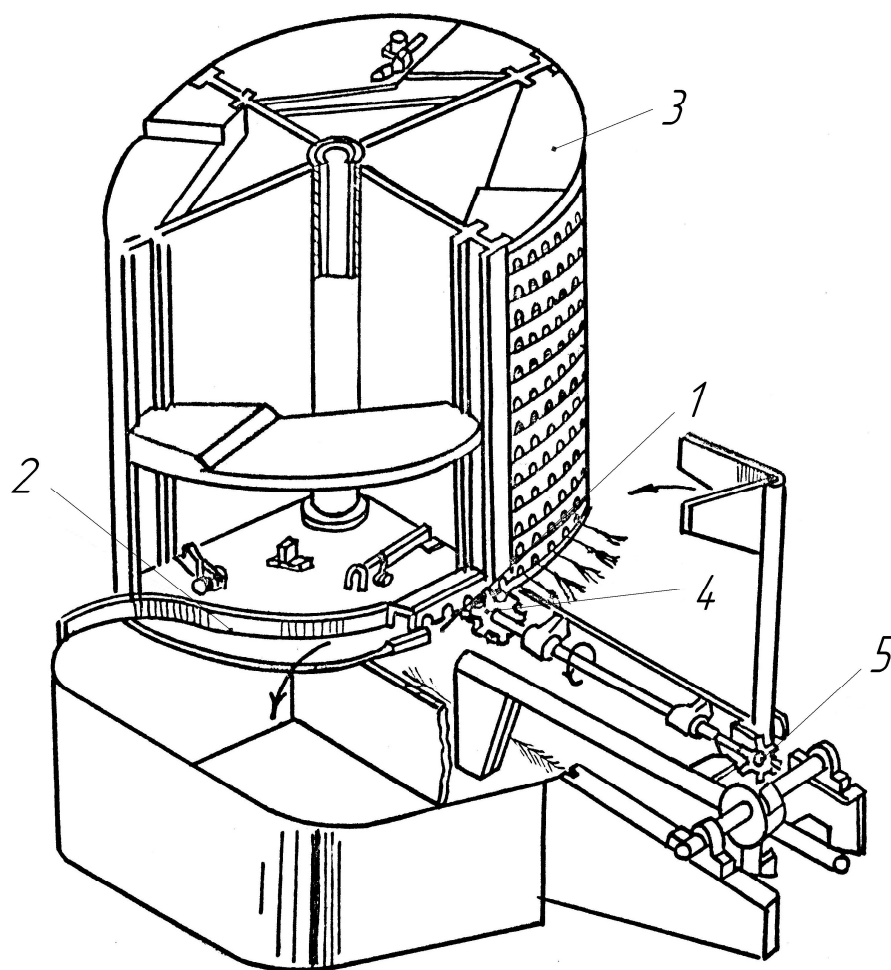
Автоматическое лесопосадочное приспособление АЛП-1
